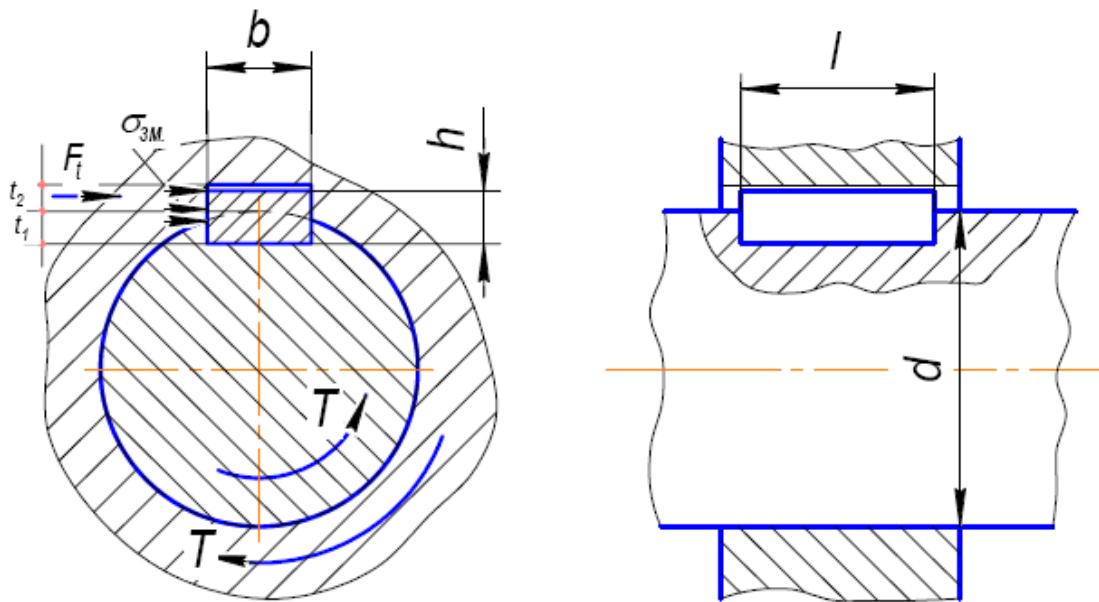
Схема сил, що діють на шпонкове з’єднання привідного вала з шестернею
